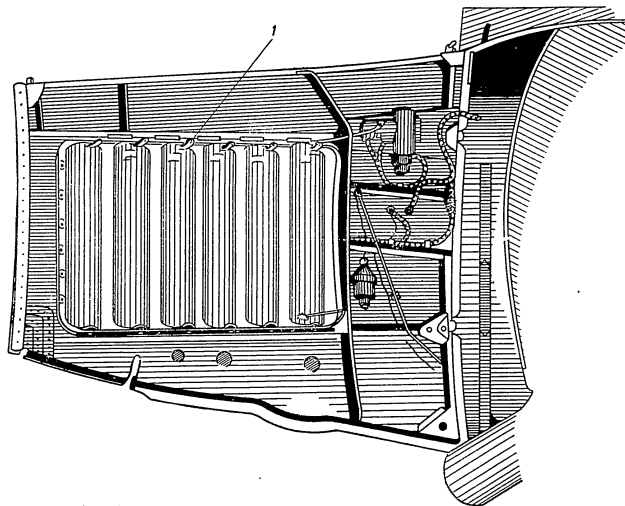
Узел соединения тяги управления жалюзи масляного радиатора двигателя с рычагом створок.
